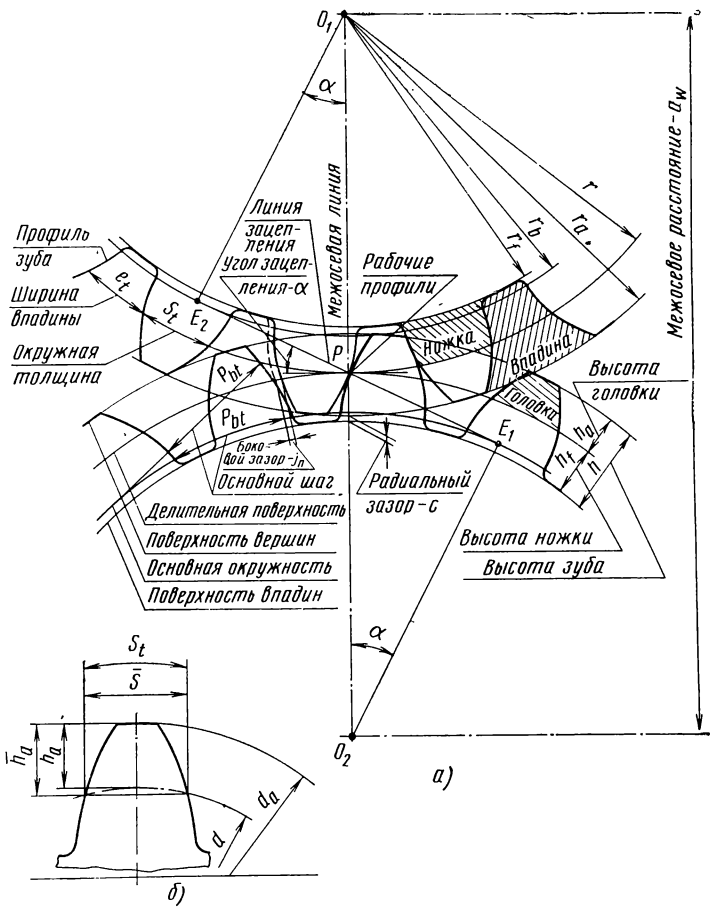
Цилиндрическая зубчатая передача внешнего зацепления:
